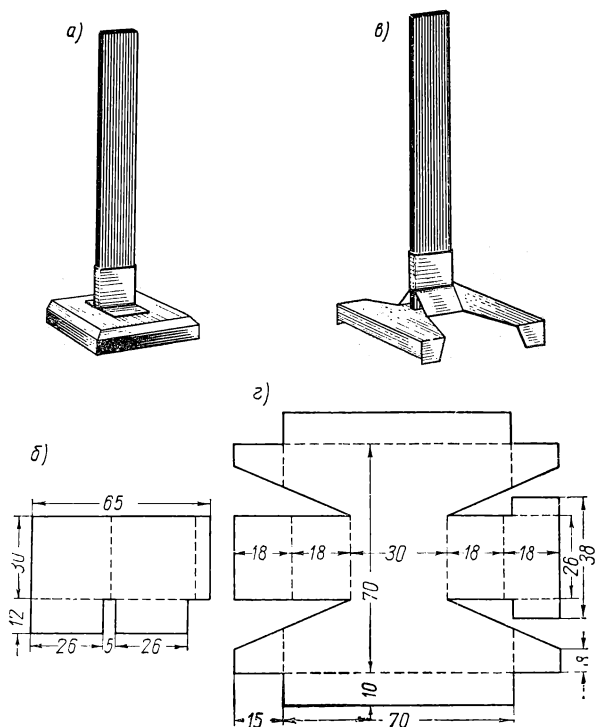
Самодельные штативы для опытов по оптике: а, в — общий вид штативов; б — фигура из жести для изготовления хомутика; г — выкройка из железа для изготовления подставки
